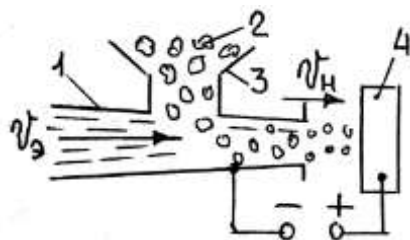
Схема подачи наполнителя к заготовке:
